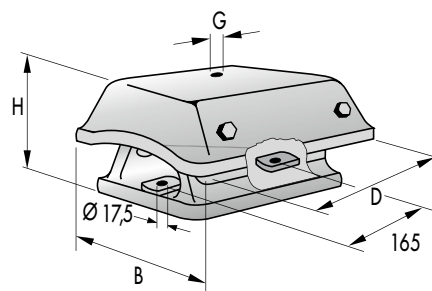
Maschinenlager 050 18 002, 050 18 004
